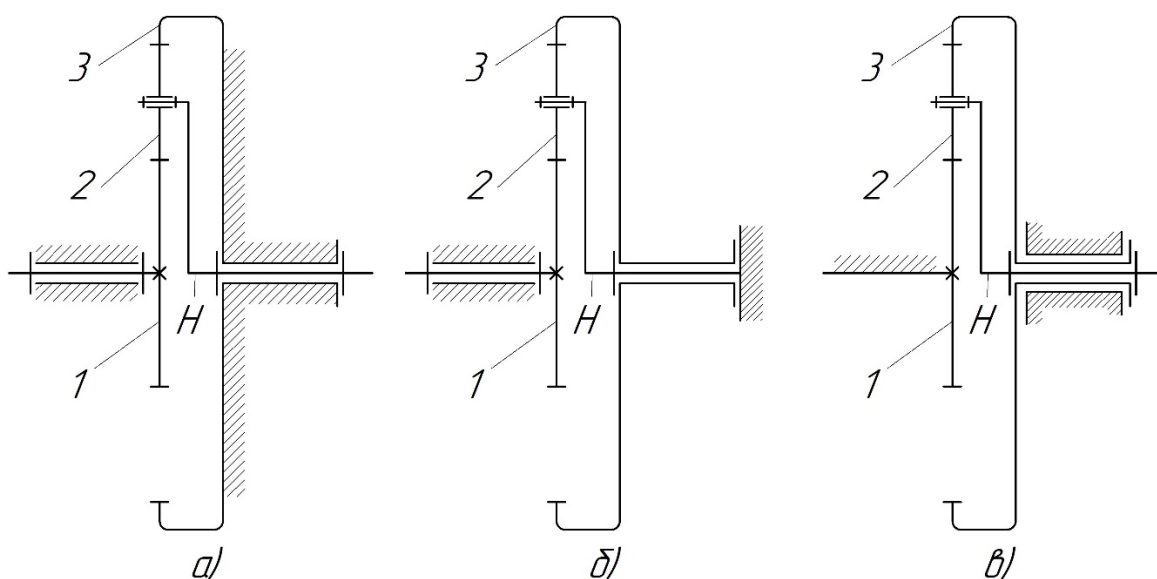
Преобразование цилиндрического планетарного редуктора
